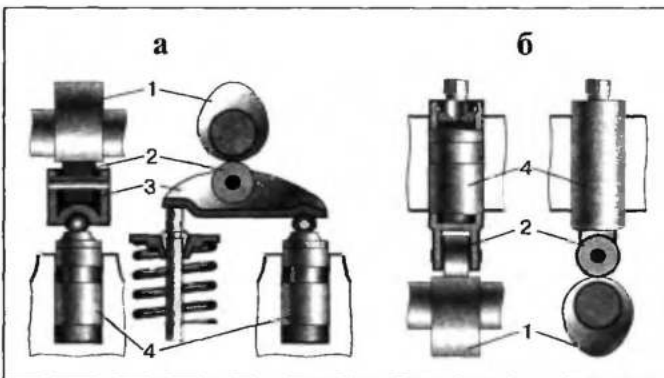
Ролики в механизмах привода клапанов: а — в схеме с рычагами; б — в схеме с нижним распределительным валом; 1 — распределительный вал; 2 — ролик; 3 — рычаг; 4 — гидротолкатель
